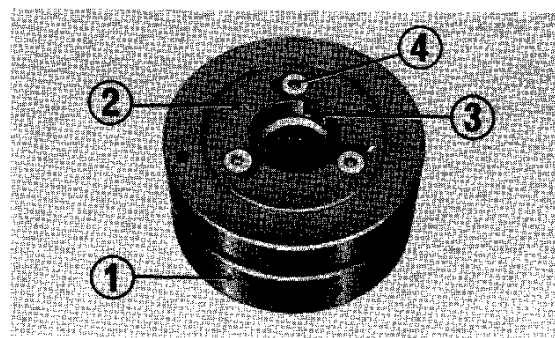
(1) Lichtmaschinen-Schwungrad
